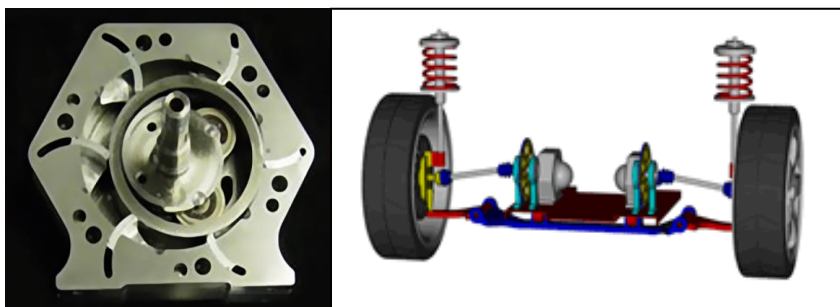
Пневмодвигатель и компоновочная схема ведущих колёс Анджело Ди Пьетро
